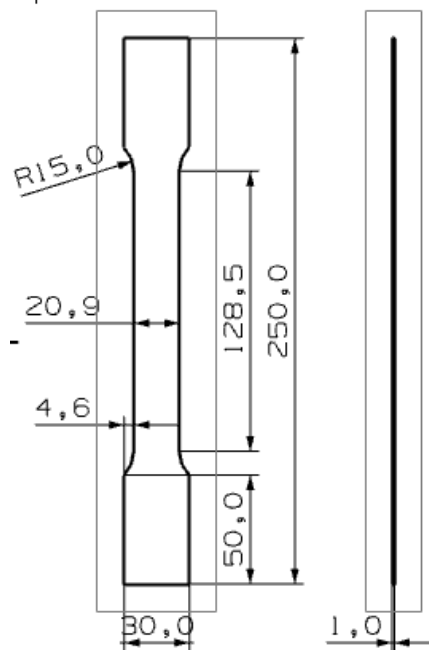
Dimensiones alzado y perfil, de las probetas troqueladas en (mm).
